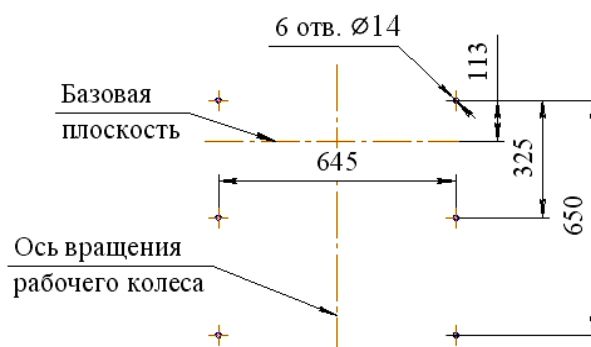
Вентиляторы ВПИ-PRU-560. Установочные размеры.
